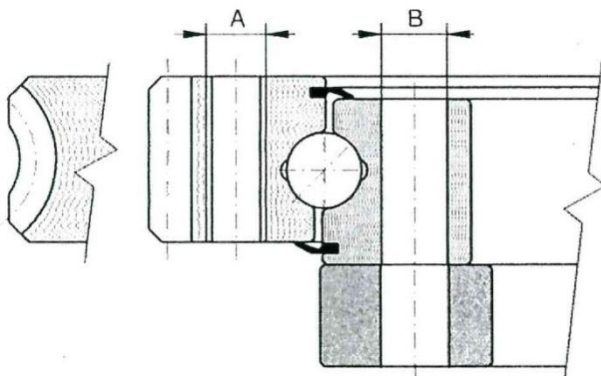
Опорно-поворотное устройство с червячным и прямозубым венцами для коренного зацепления
